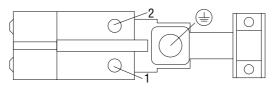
Anschluss Fremdlüfter (Sicht von oben)
